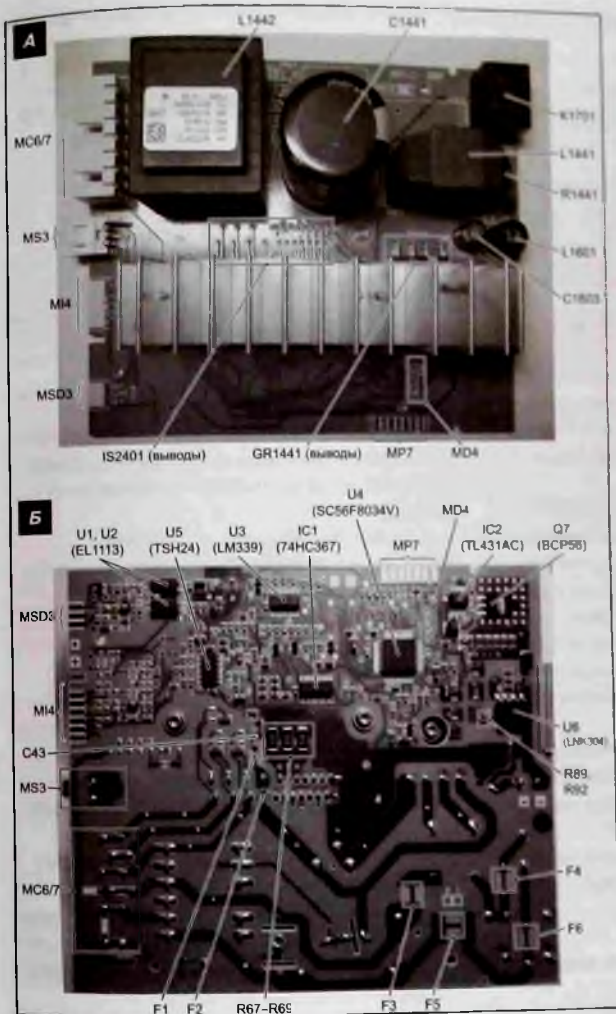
Внешний вид ЭМ AKO737117-04, его основные компоненты и соединители, где: а – вид сверху; б – вид с обратной стороны
